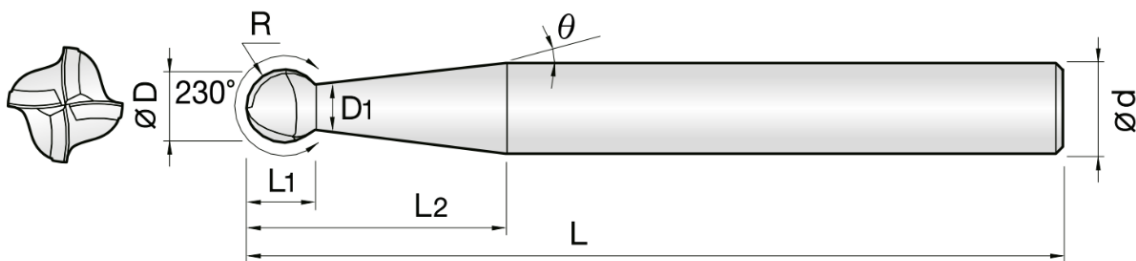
Toroidná fréza pre rebrovanie do 68 HRC od PM-TECH [33].
